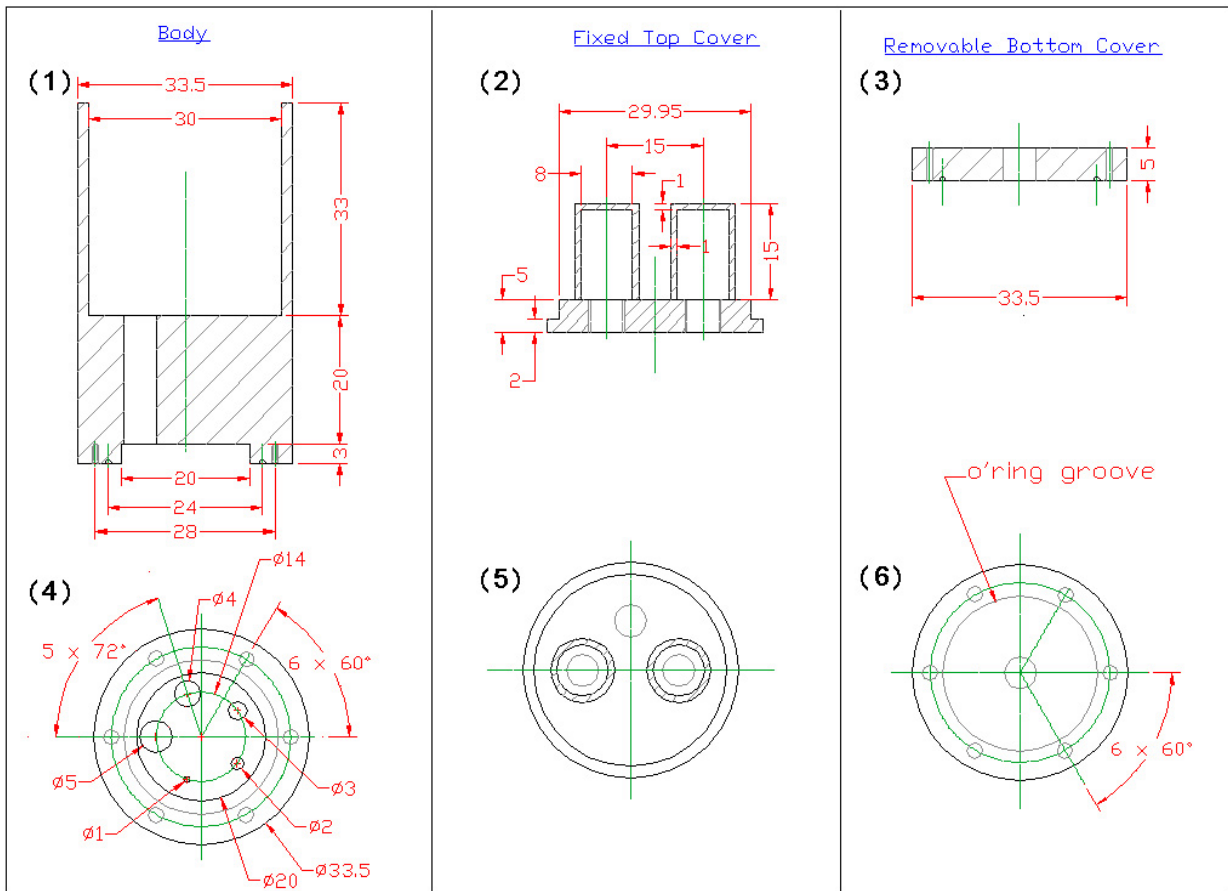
Dibujos esquemáticos del maniquí de calidad de imagen NEMA. Cortes coronal y transversal del cuerpo principal (1) y (4); tapa superior (2) y (5); tapa inferior (3) y (6). Todas las dimensiones están en milímetros con una tolerancia de 0.1 mm (Nema, 2008).
